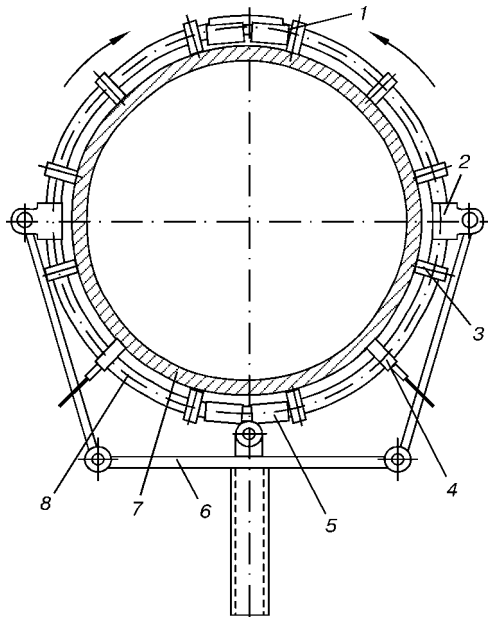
Устройство на основе УКЗ типа «клещи» для резки труб: 1 — соединитель полуколец УКЗ; 2 — шарнир; 3 — бобышка для установки фокусного расстояния; 4 — то же с гнездом для электродетонатора; 5 — шарнирный замок; 6 — устройство для сочленения и фиксации полуколец УКЗ; 7 — разрезаемая труба; 8 — полукольцо УКЗ
